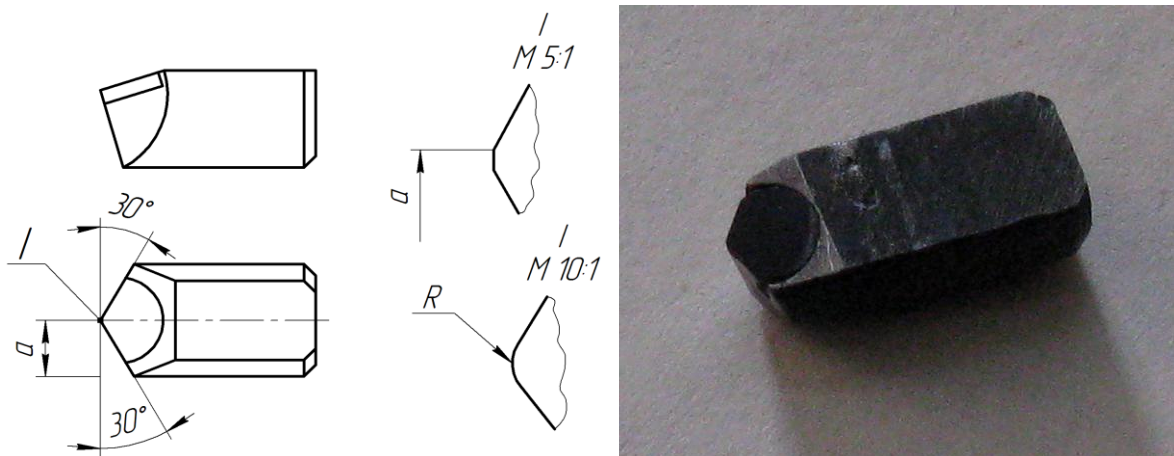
Конструкция и общий вид универсальной резцовой вставки с напаянной пластинкой СТМ К02Д «Белбор»
